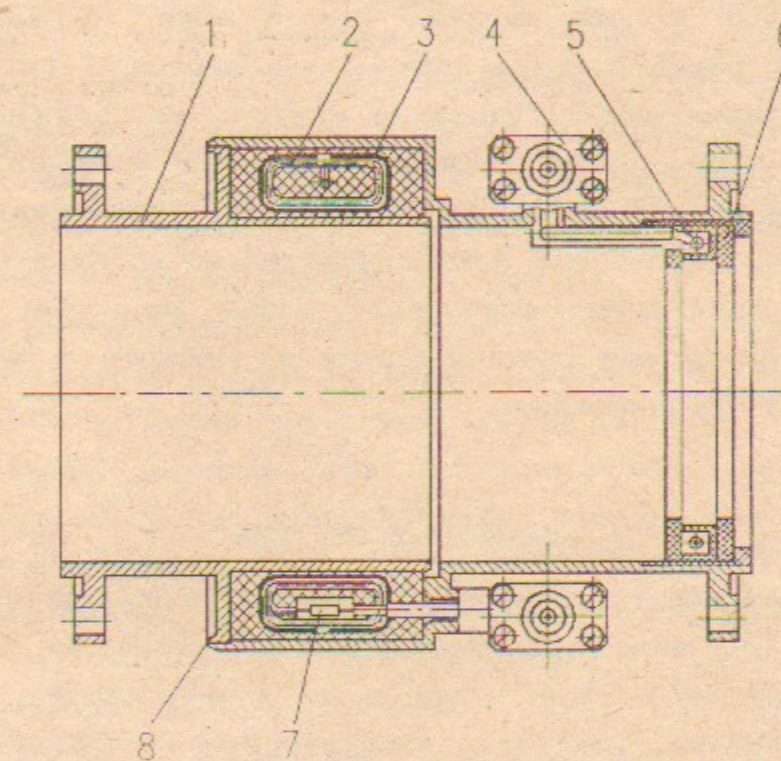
Конструкция диагностического блока. 1 - корпус; 2 - пояс Роговского; 3 - электростатический экран; 4 - вакуумный разъем с двойной изоляцией; 5 - диамагнитный зонд; 6 - стеклянные диафрагмы; 7 - сопротивление нагрузки пояса; 8 - сварное соединение.
